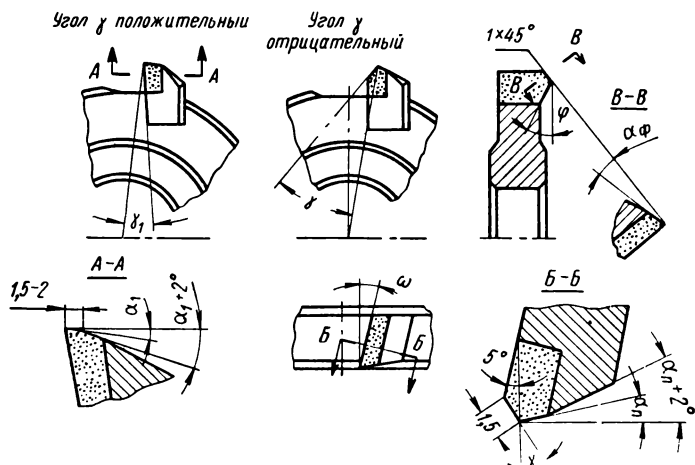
Геометрические параметры режущей части дисковой фрезы с пластинками из твердого сплава
